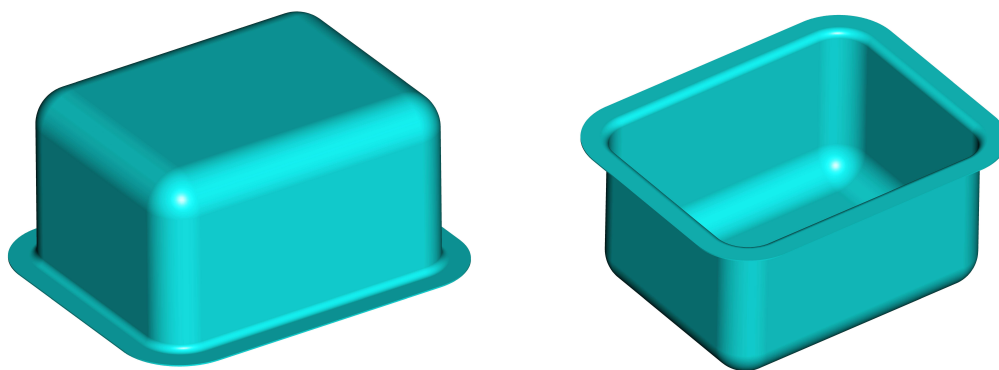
Skica krytu řemenového převodu - stav před svařením
